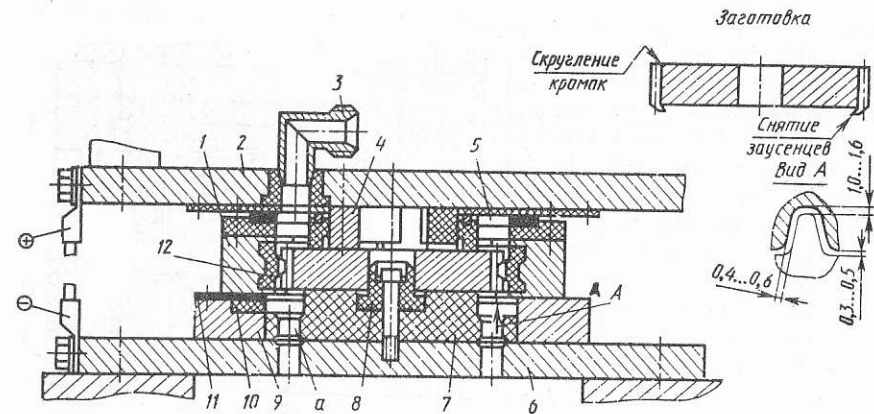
Приспособление для скругления кромок и снятия заусенцев травлением под корень
